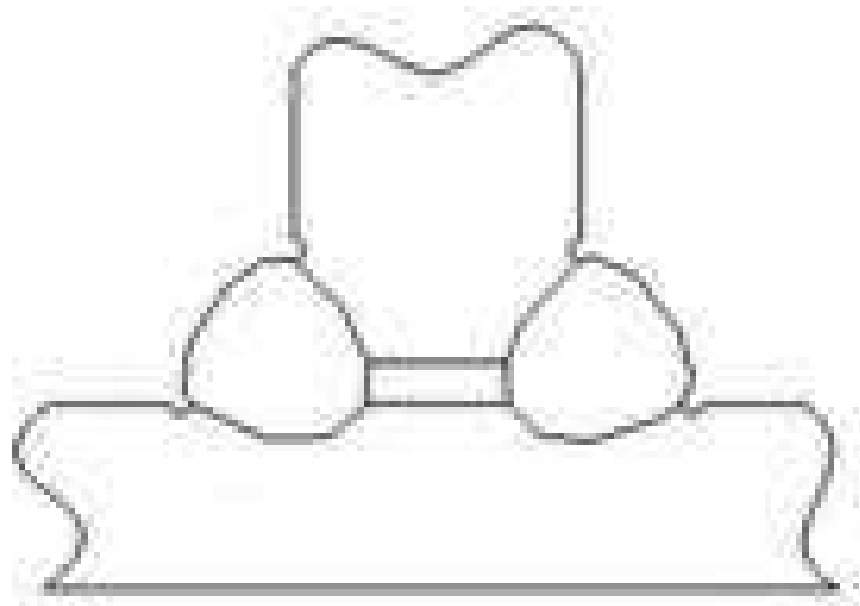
Схема сварных швов с подрезами
